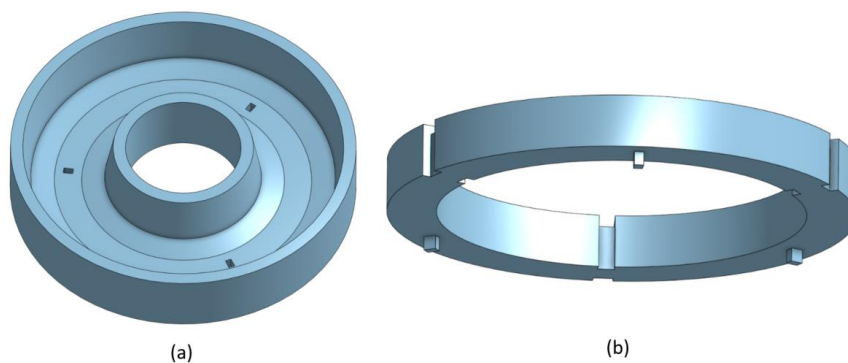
Moule en PLA pour la fabrication des supports en silicone - partie fixe (a) et partie mobile (b)
